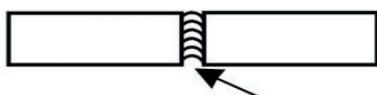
Конструктивный концентратор напряжения – незаваренный сварной шов
